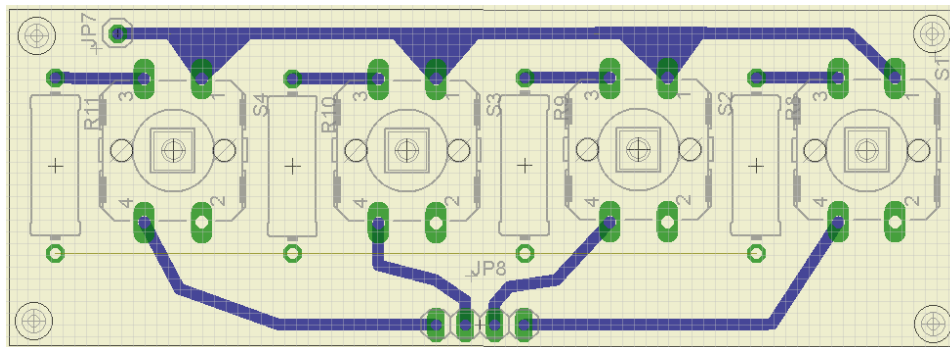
Esquema EAGLE da PCB 2 para impressão
